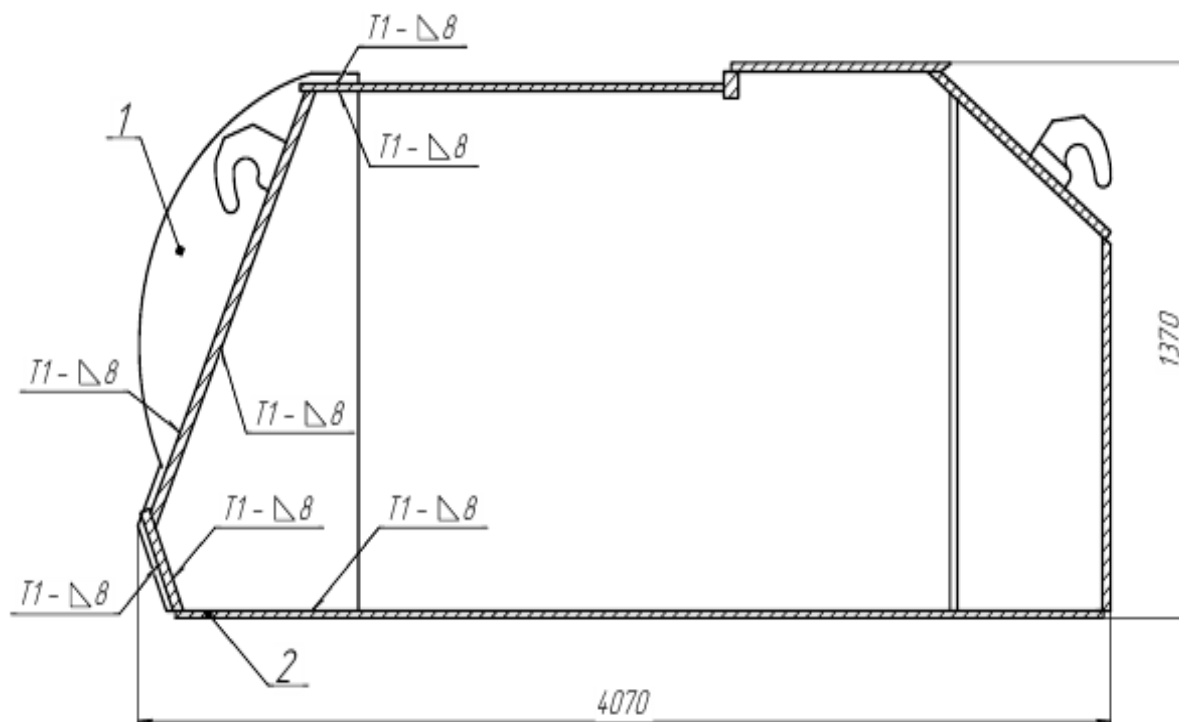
Розріз зварного корпусу спеціальної техніки типу «Ковпак»: 1 – верстат; 2 – листи вежі
